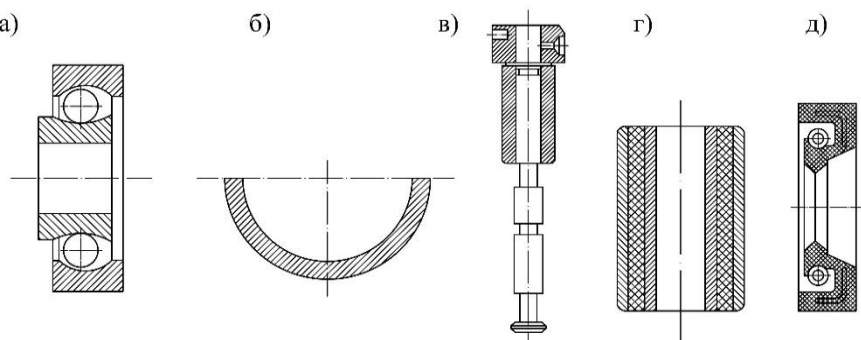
Типовые сборочные соединения механического оборудования
